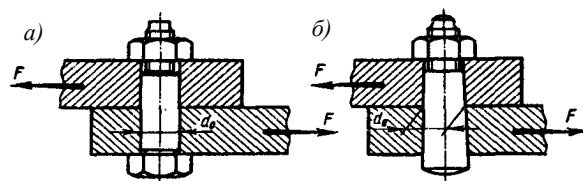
Схема для расчета болтов, поставленных без зазора в отверстия из-под развертки
